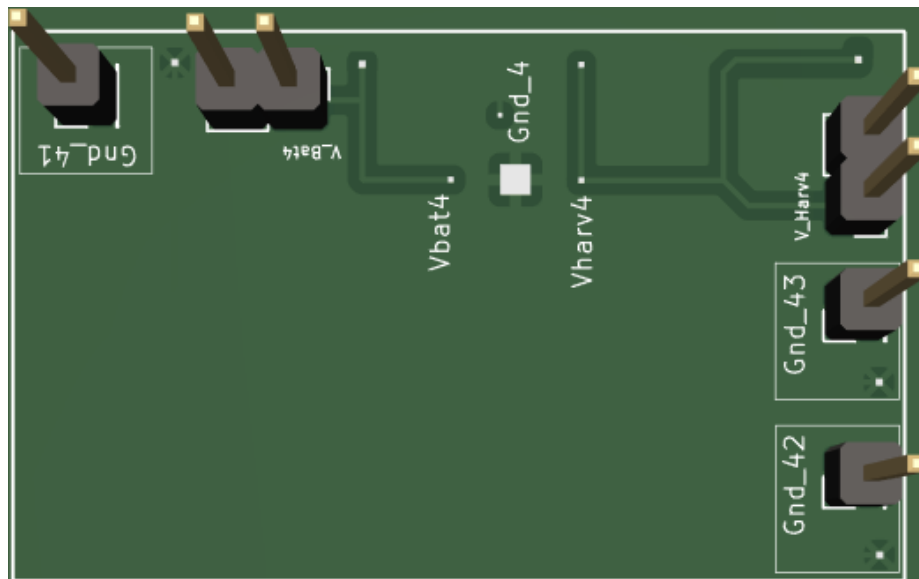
Vista 3D de Segunda Versión Diseño de PCB.
